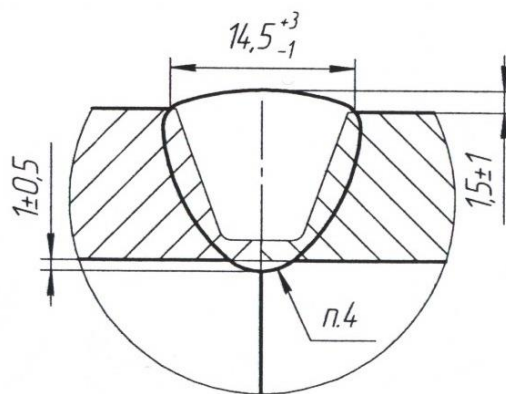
Сварной шов для толщины 11,5 мм
